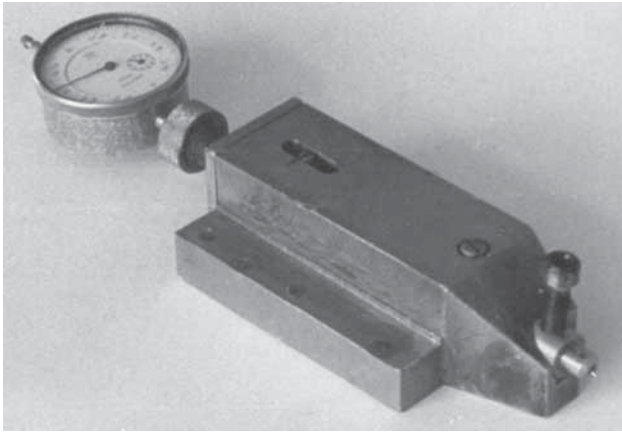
Пружинная оправка для алмазного выглаживания цилиндрических и торцевых поверхностей
